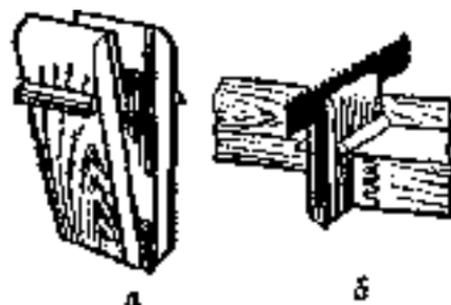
Тиски для заточки пилы (а) и установка тисков и положения (б).
